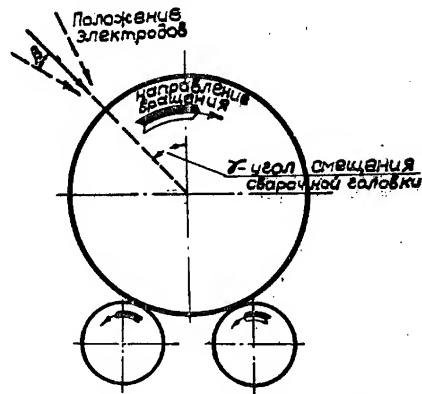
Схема сварки поворотного стыка трубы.
